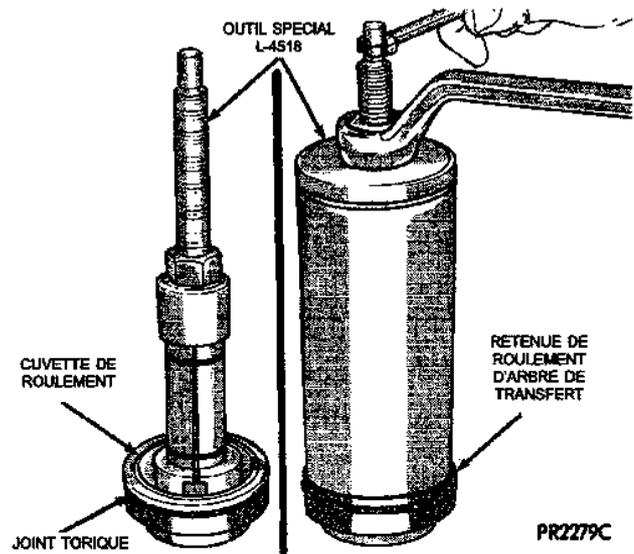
Dépose de la cuvette de roulement d'arbre de transfert
